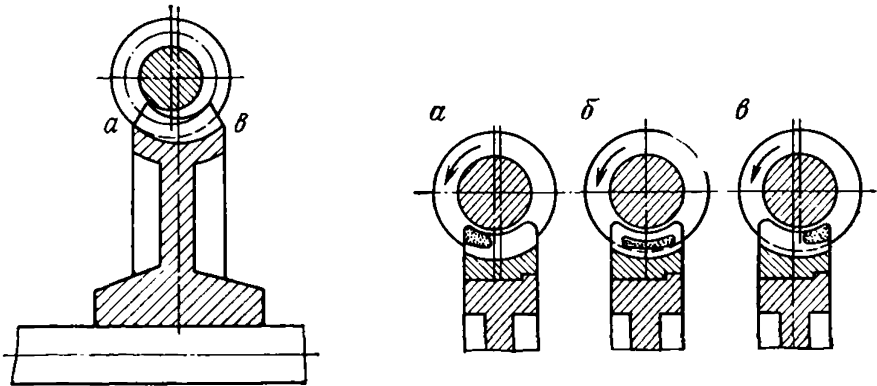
Проверка взаимного положения червячного колеса и червяка
